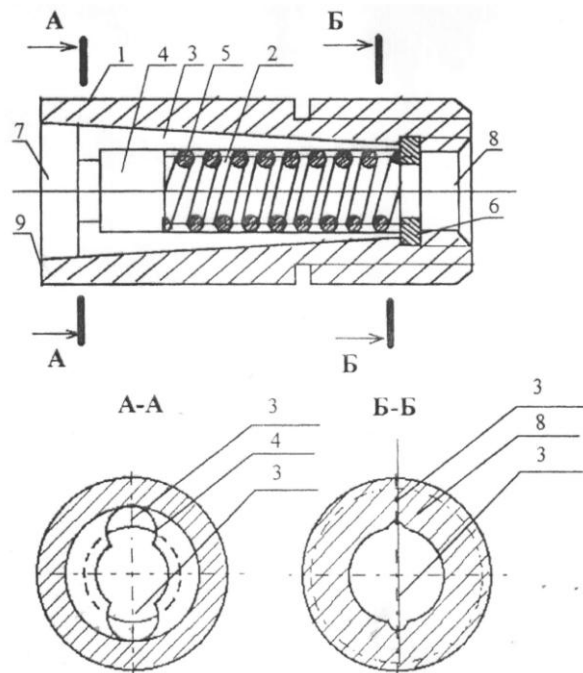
Схема запорно – регулирующего устройства: 1 – корпус; 2 – канал; 3 – дроссельные каналы переменного сечения; 4 – плунжер; 5 – пружина; 6 – винтовое звено; 7 – вход; 8 – выход; 9 – плоскость
